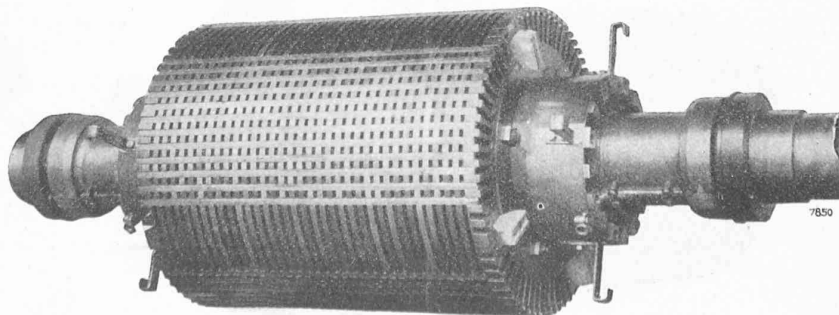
Rotor d'un turbo-alternateur, 1 500 t/m, sans enroulement.
